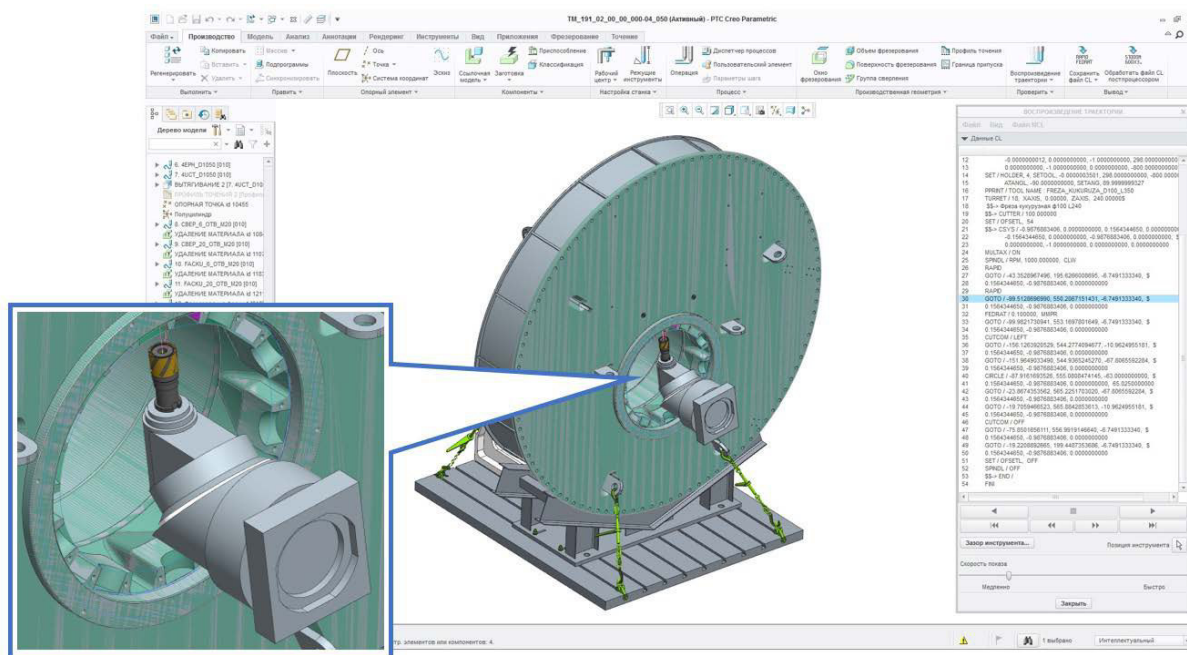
Фрезерование пазов корпуса винторулевой колонки в САМ-модуле Creo Parametric
